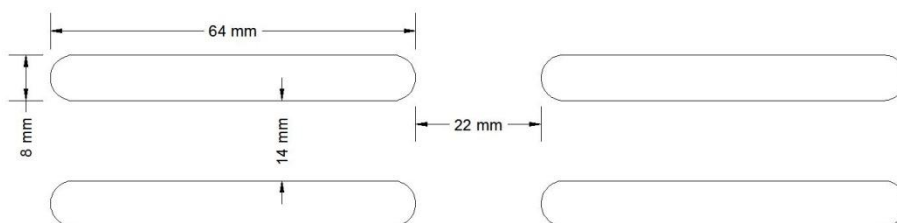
Pormenor da furação de um painel tipo CFR.
